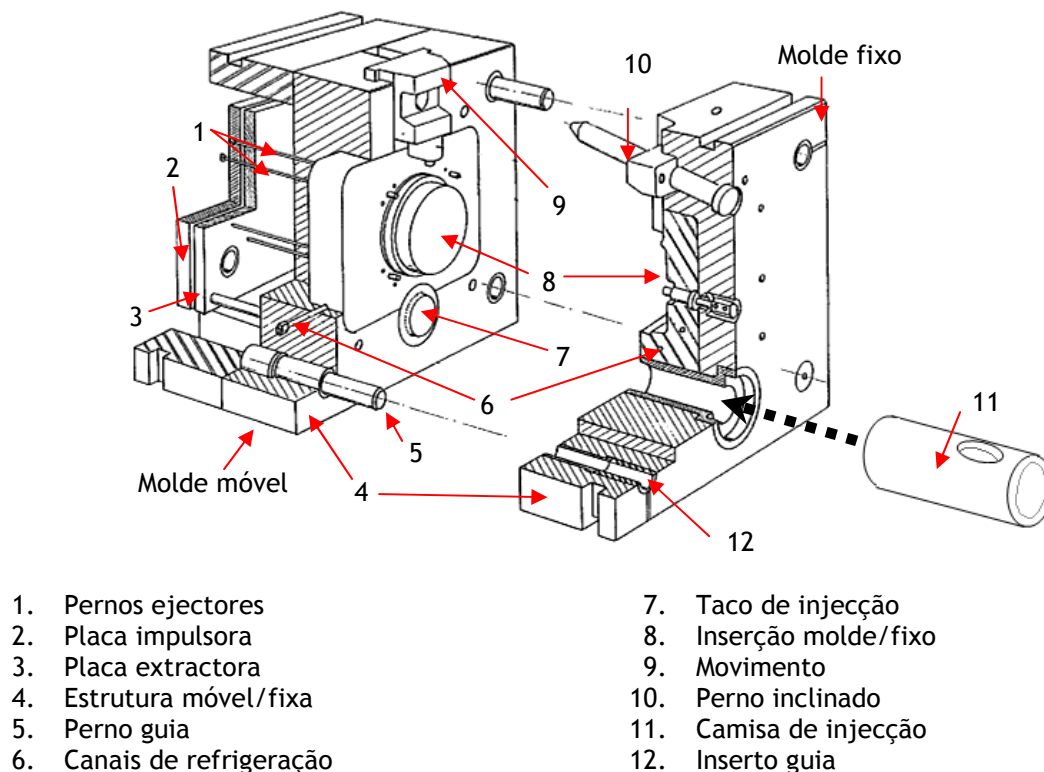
Esquema do molde no processo de fundição injectada [7]
